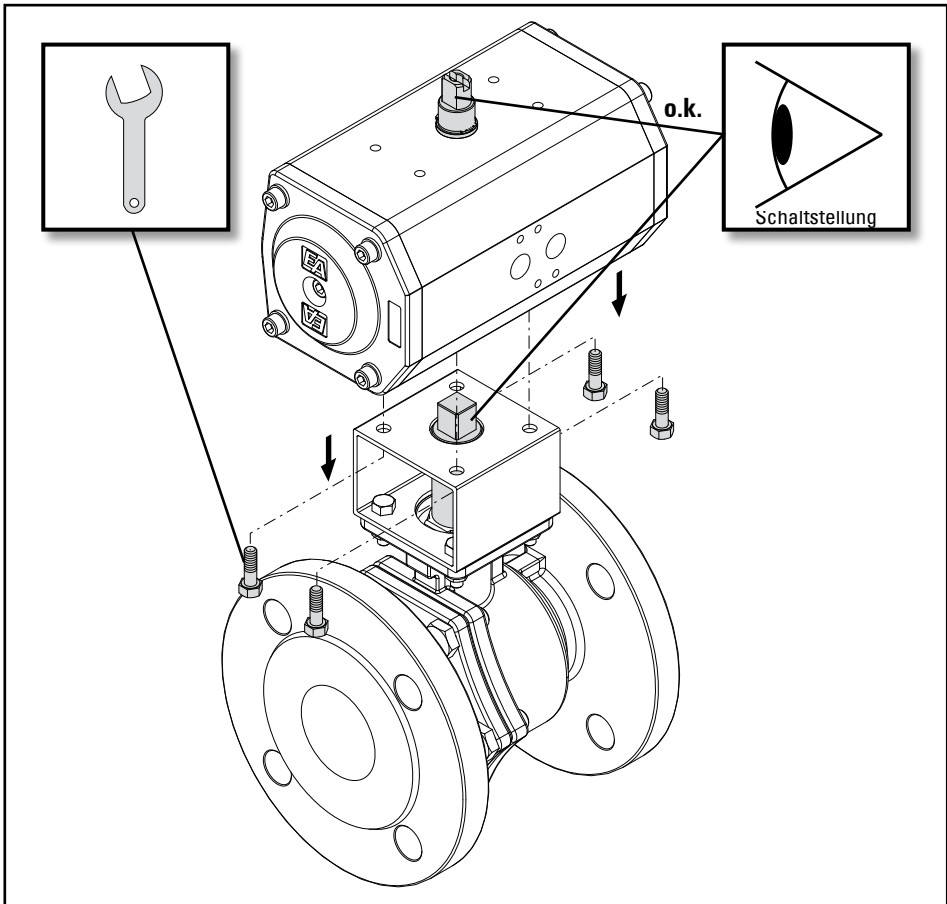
Montage / Demontage, Montage mittels Konsole und Spindel
